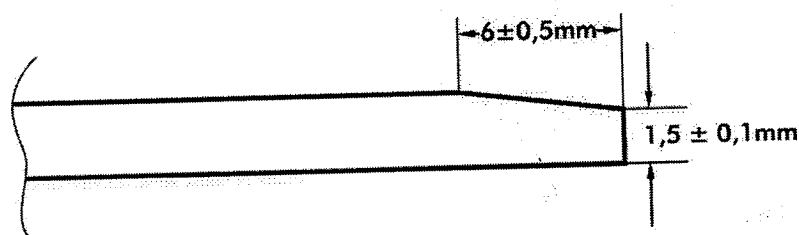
Dimensões do chanfro desquinado tipo a fio
